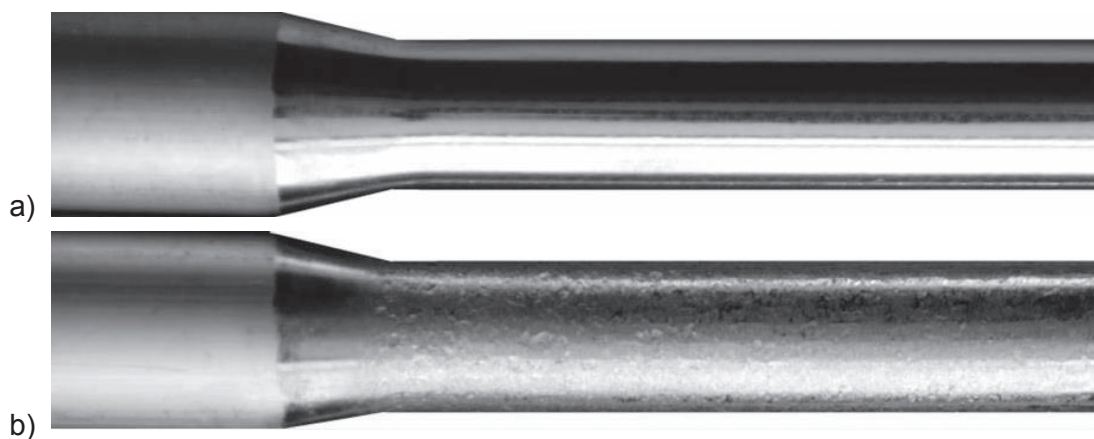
Ausschnitt eines Aluminiumwerkstücks, umgeformt mit konventionellen Werkzeugen ohne Wolframcarbid-Kobalt-Schicht bei $v_f = 500$ mm/min; a) Nass, b) Trocken.
